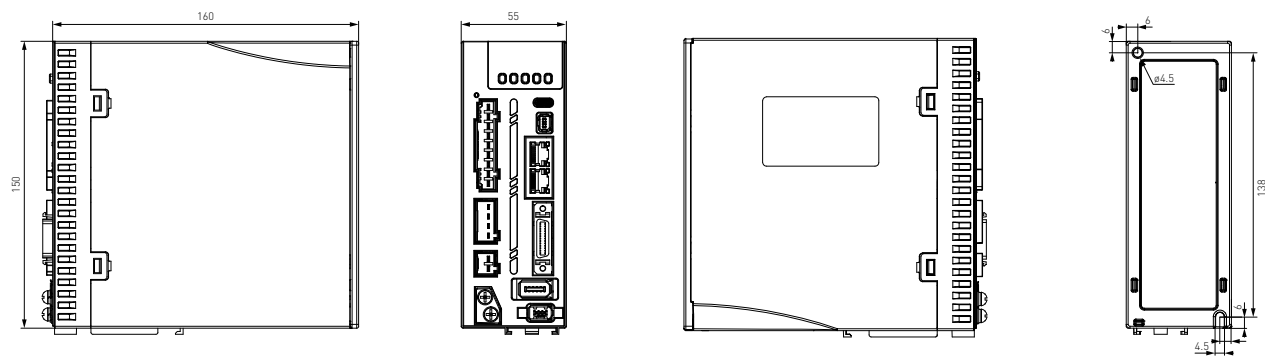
Габаритные размеры драйверов EL8-EC750F и EL8-EC1000F.
